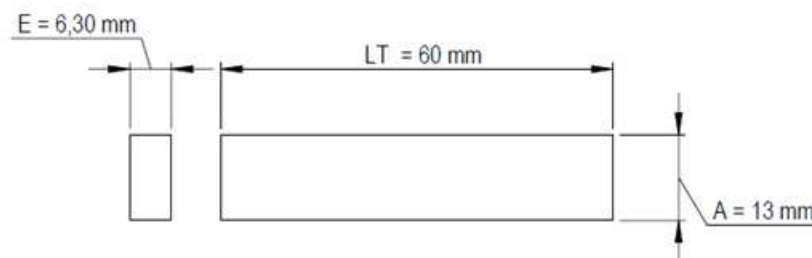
Geometría y dimensiones para probetas a impacto.
